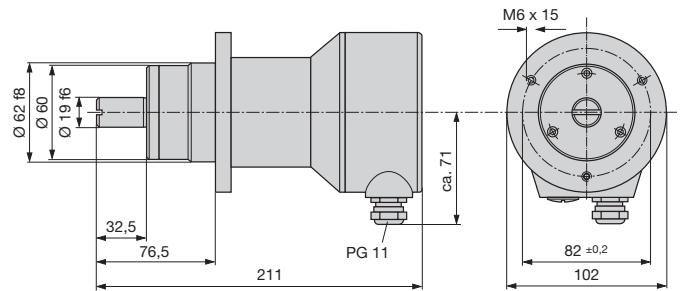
KINAX WT 717 mit Zusatzgetriebe.
